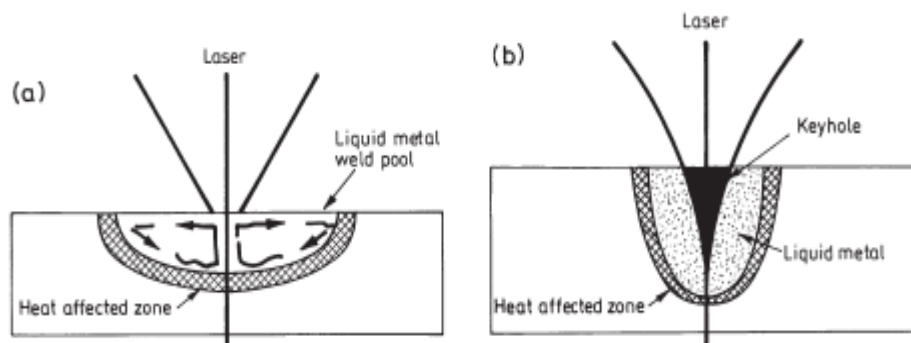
soudure par conduction de fusion (a) et soudure par pénétration profonde (trou) (b).
